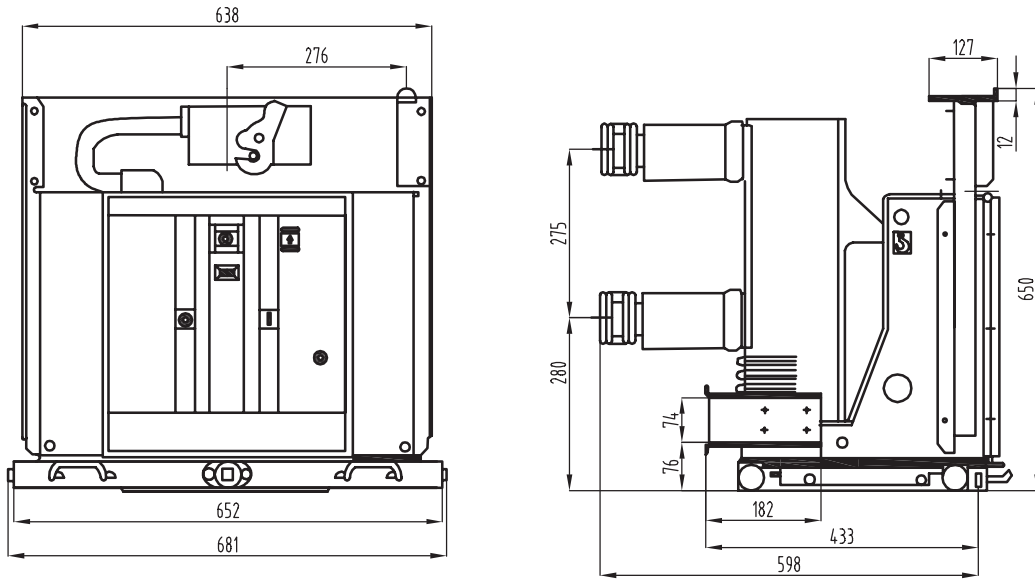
Габаритный размер выключателя ВВ-12 выкатного исполнения для ячейки шириной 800 мм
